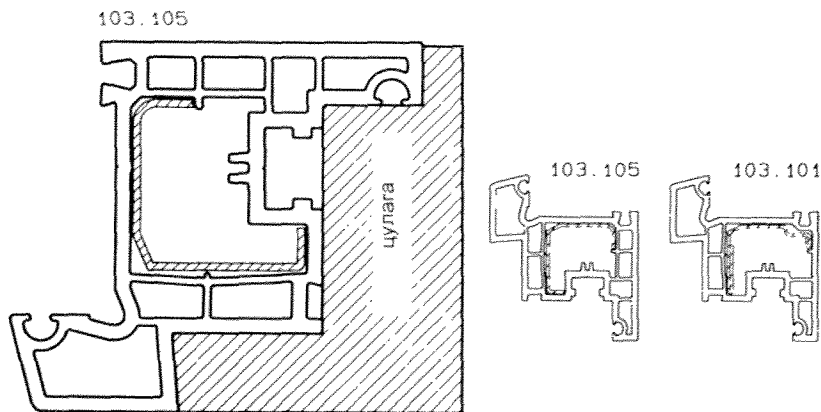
Сварочная цулага для профиля створки
